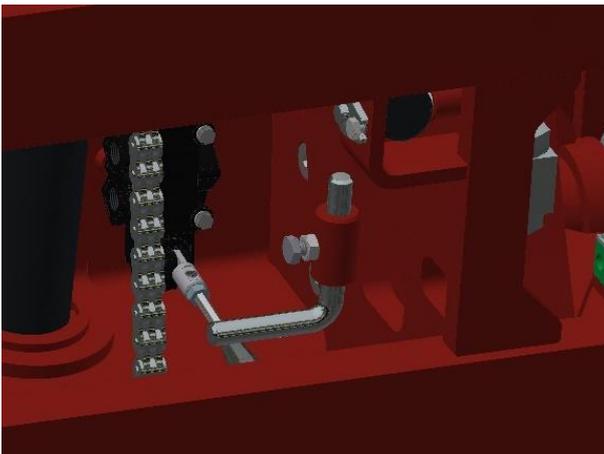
Hydraulischen Endanschlags/Schalters
